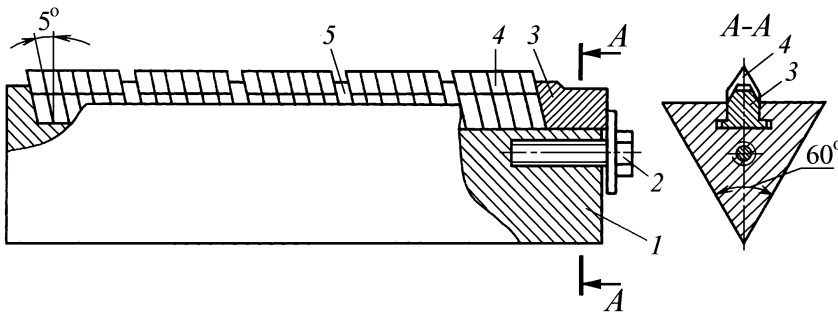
Кассета для затачивания резьбовых пластин:
